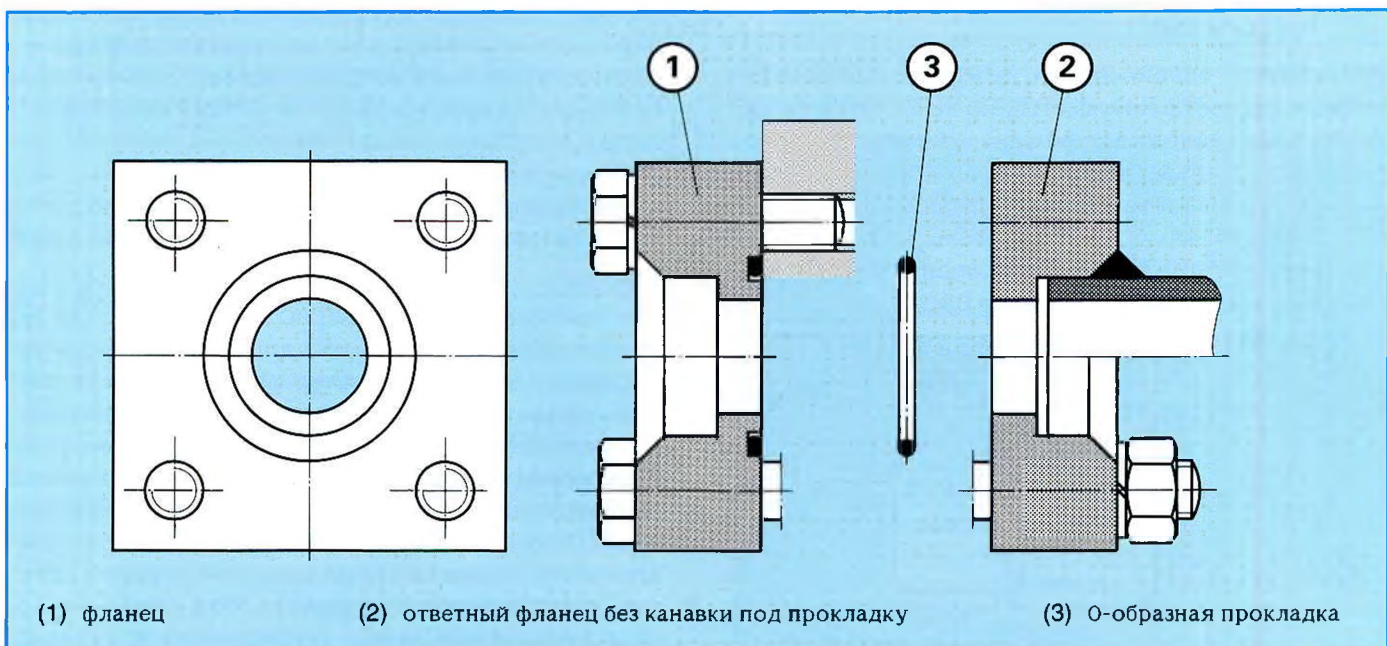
Квадратный фланец и фланцевое соединение. Фиксация осуществляется при помощи соединительных болтов. Соединение фланца с трубой выполнено на угловом сварном шве. Уплотнение эластичное, обычно для этого используется O-образная прокладка
